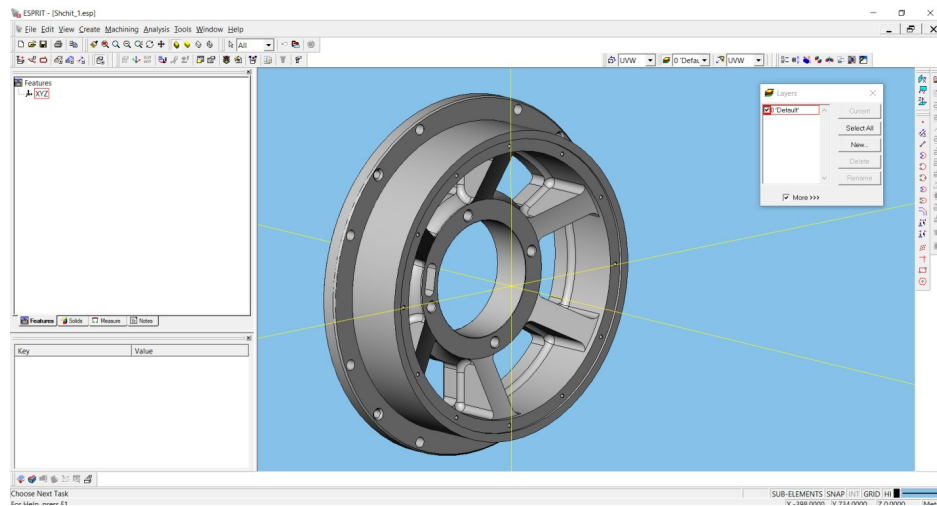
3D-модель деталі «Корпус підшипника» у середовищі САМ ESPRIT
